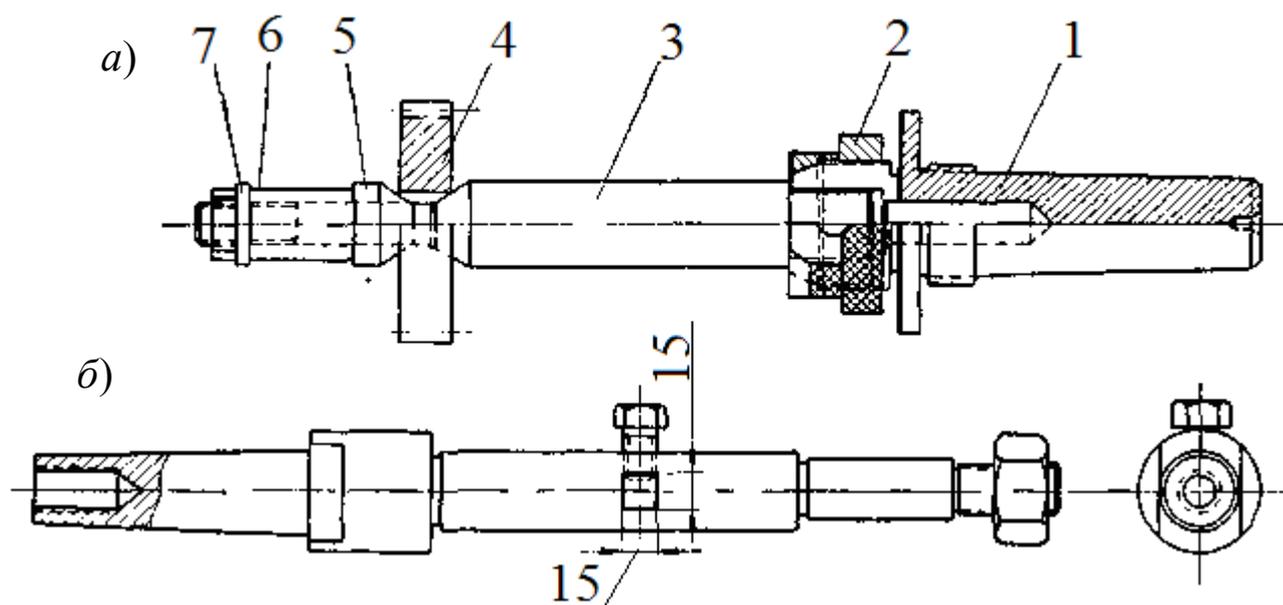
Схема приспособления для закругления торцов зубьев колес на зуборезных станках
